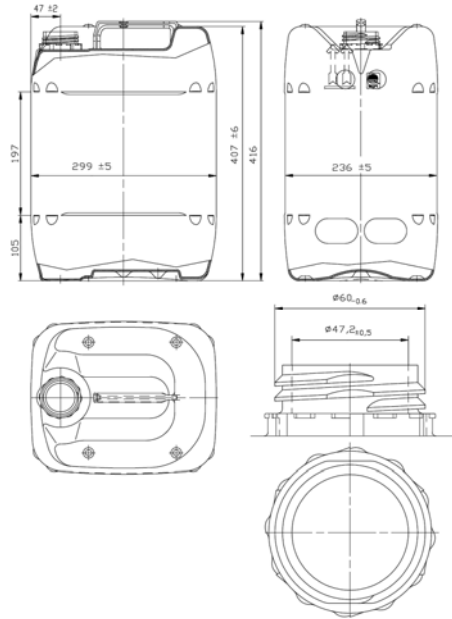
Zeichnung der 22 l-Kanister (Baumuster 1)
